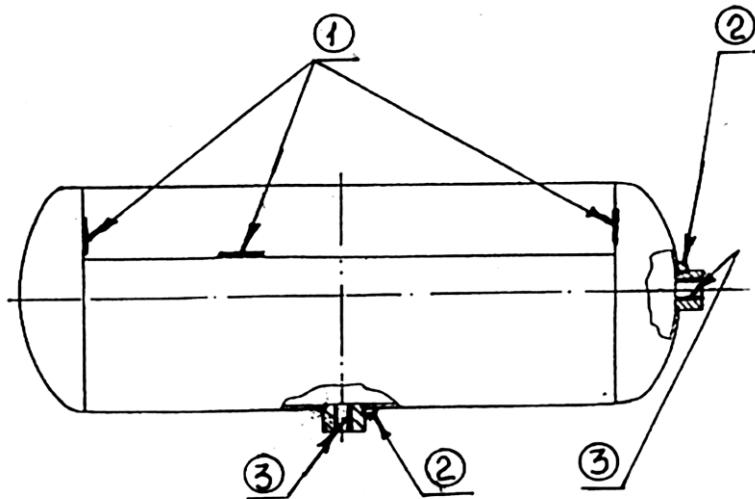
Дефекты воздушного резервуара марки Р7-782, ремонтируемые сваркой или наплавкой
